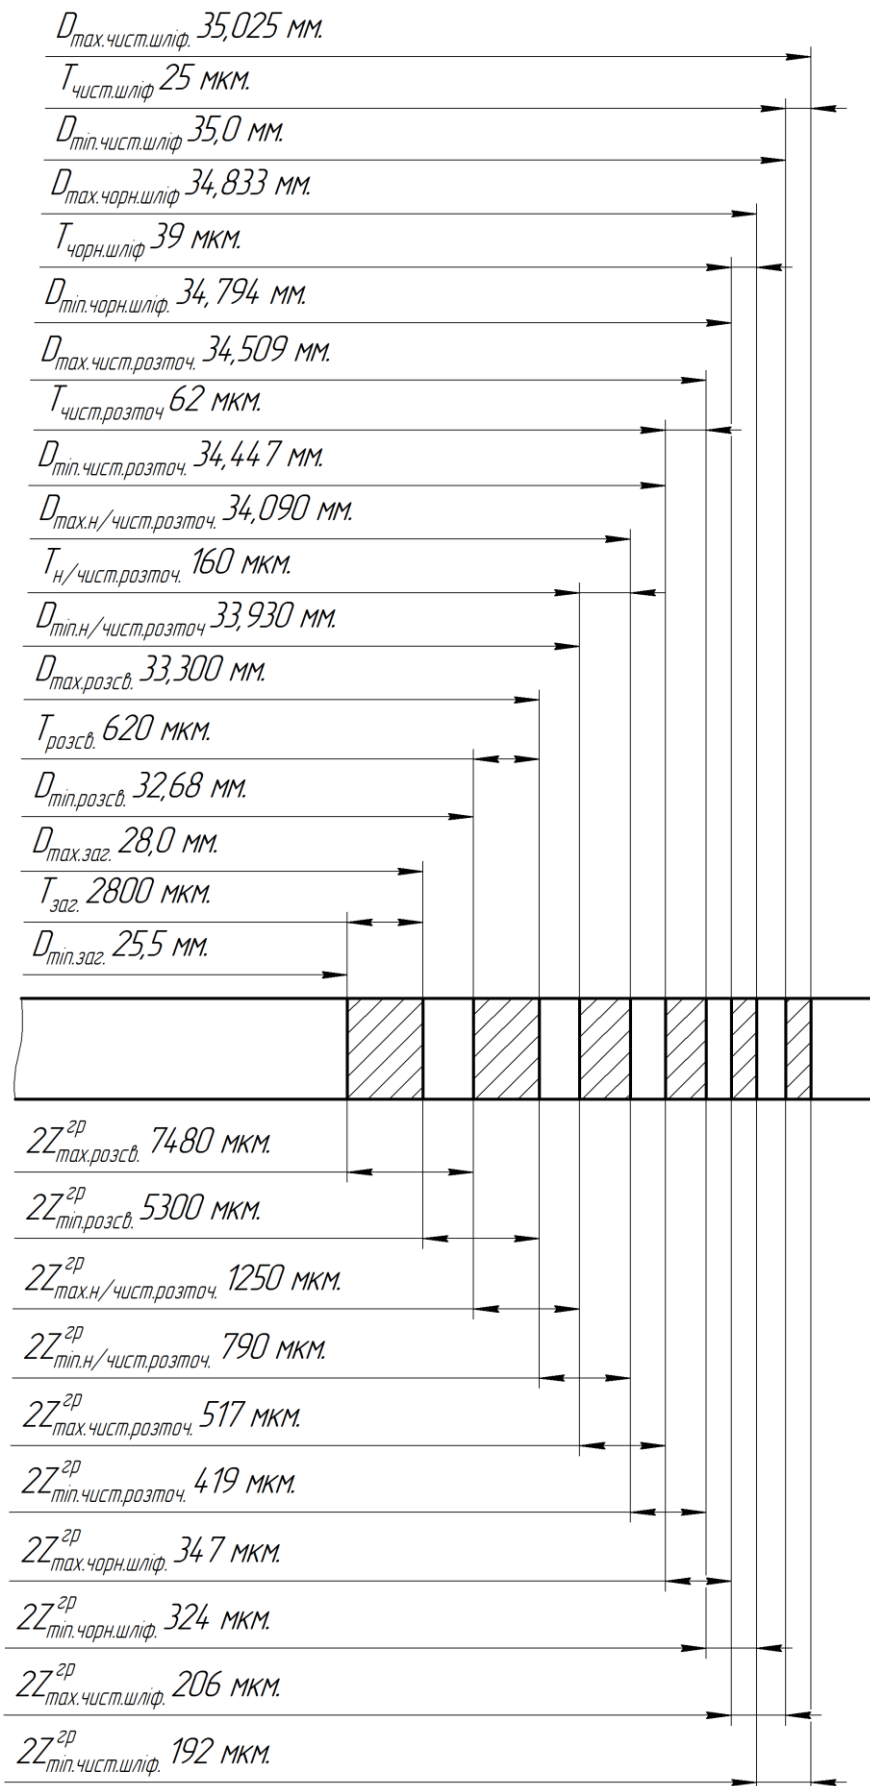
Схема розташування полів допусків і припусків для поверхні $\varnothing 35^{+0.025}$ мм.
